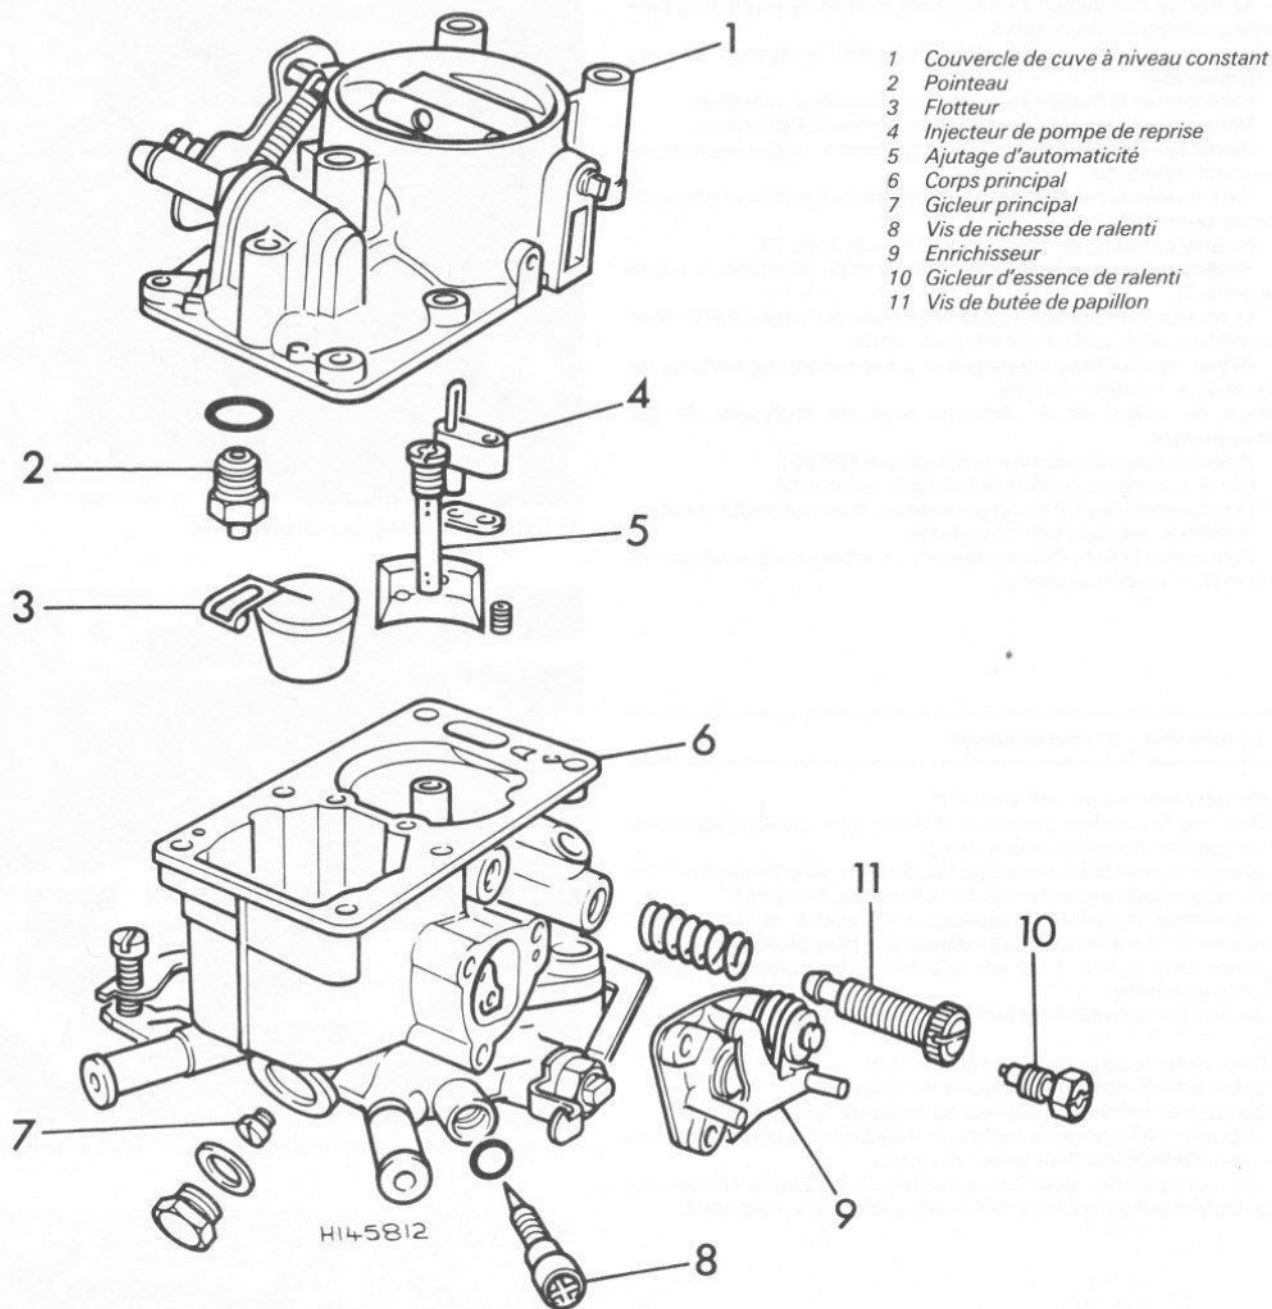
Eclaté du carburateur Solex 32 PBISA
